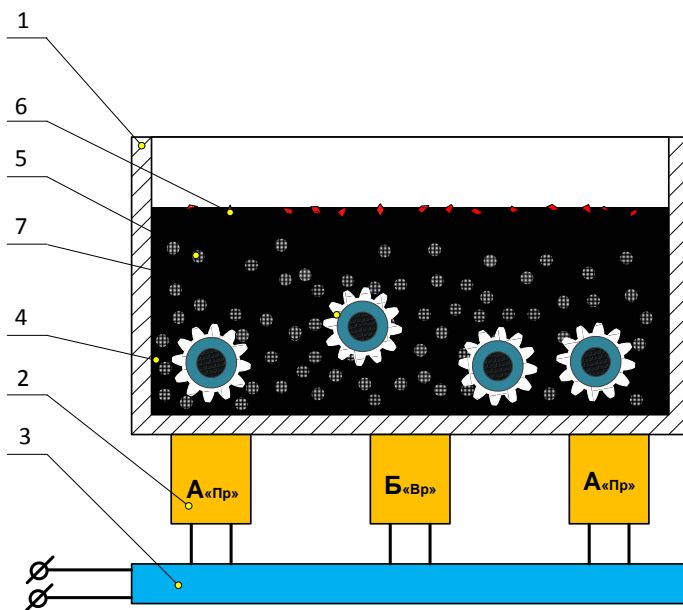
Схема установки для финишной обработки изделий из металлов:
